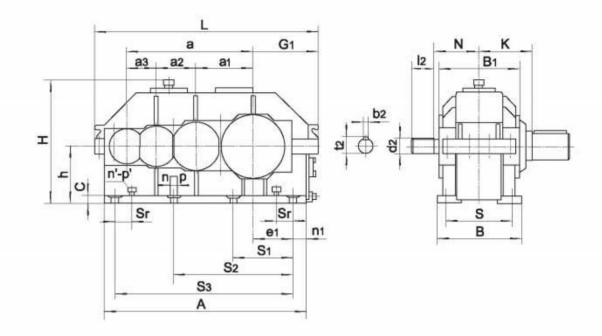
QY3D减速器外形尺寸 Figure 9 External dimension of QY3D decelerator
